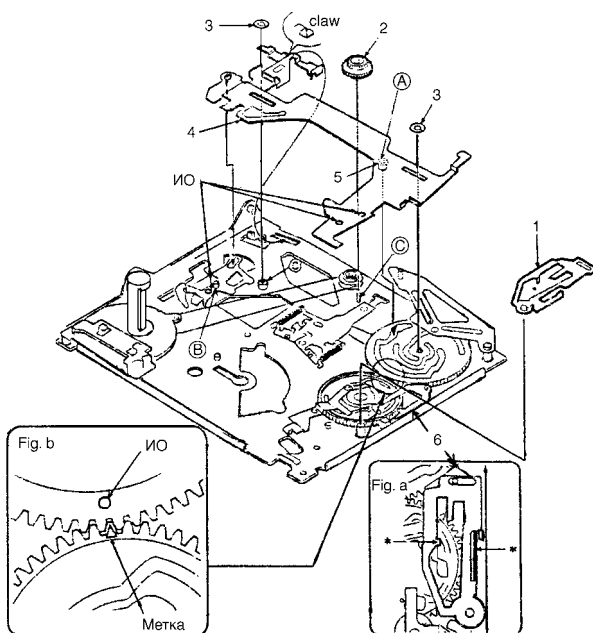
Демонтаж и установка пластины регулятора натяжения (2), перекидной шестерни и узла ползуна М
